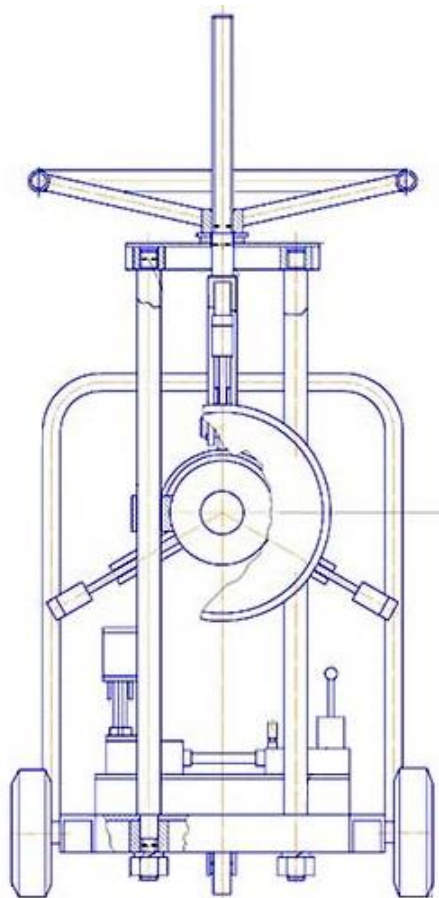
Загальний вигляд станда (вигляд спереду)
